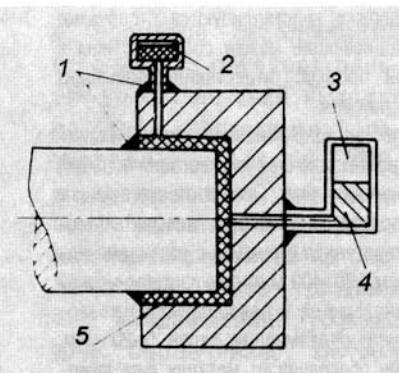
Схема автовакуумной пайки: 1 — герметизирующие сварные швы; 2 — сорбционный насос; 3 — питатель; 4 — припой; 5 — паяльный зазор с порошком
